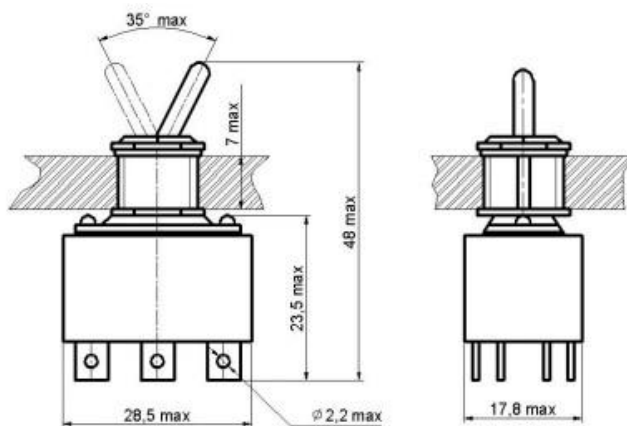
габаритные и установочные размеры тумблера ТП2
